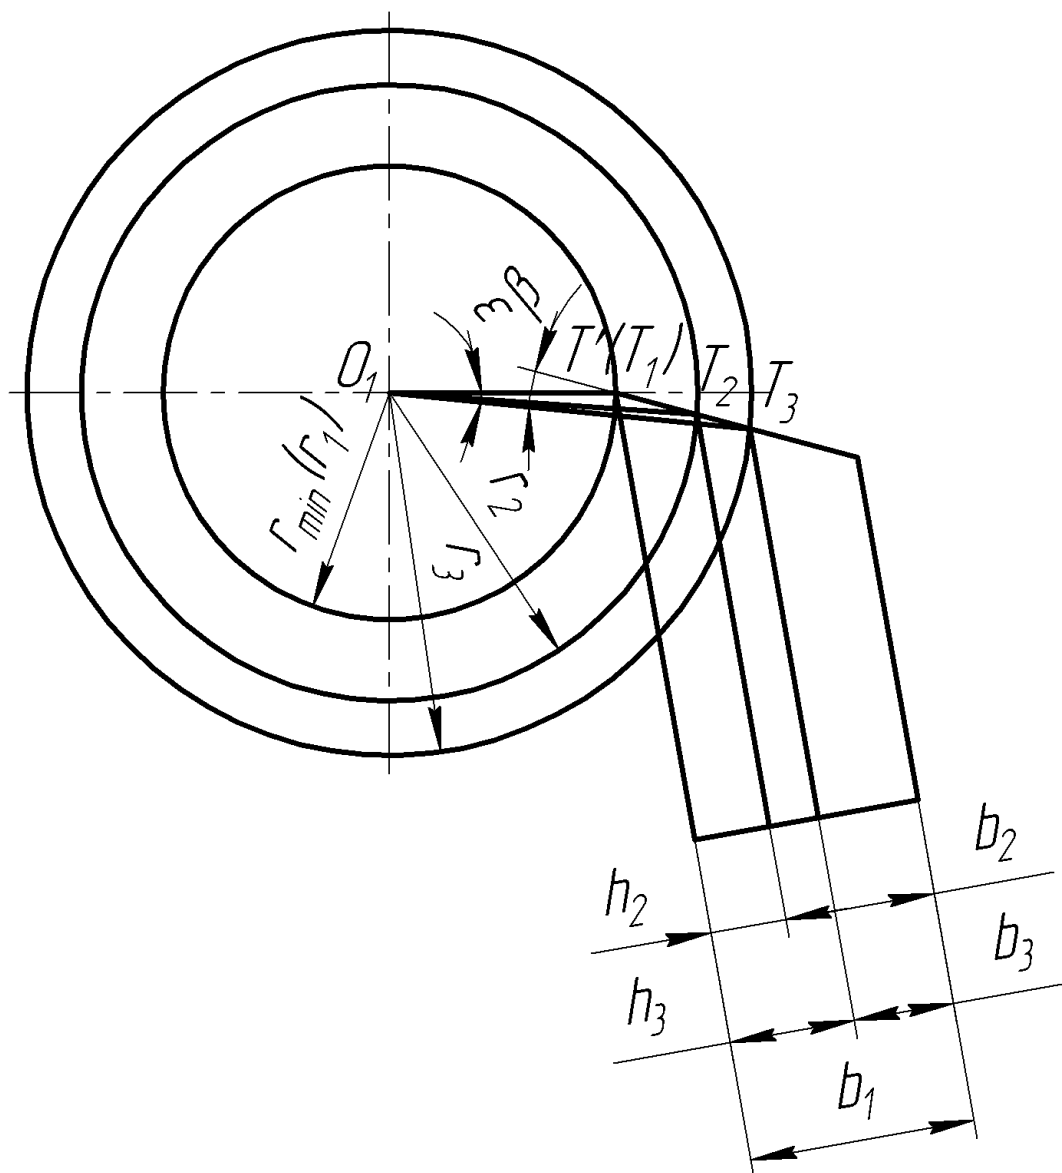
Розрахункова схема профілю призматичного різця
